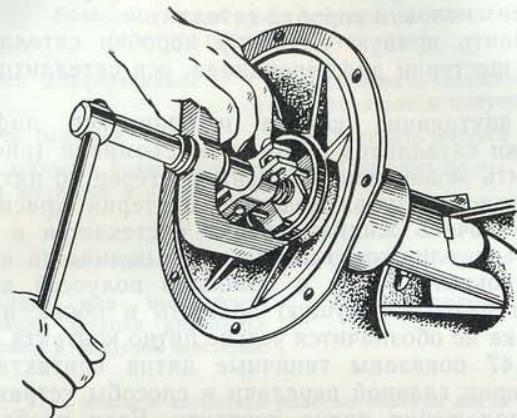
Выпрессовка наружного кольца подшипника дифференциала
